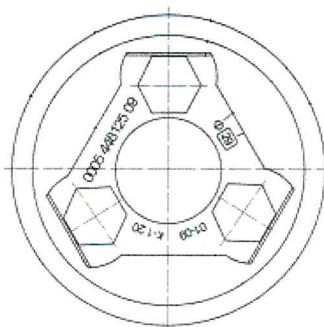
Внешние отличительные признаки буксового узла с подшипником кассетного типа в габаритных размерах 150x250x160 мм торговой марки BRENCO (ЕПК- BRENCO) под адаптер для крепления тремя болтами М24
